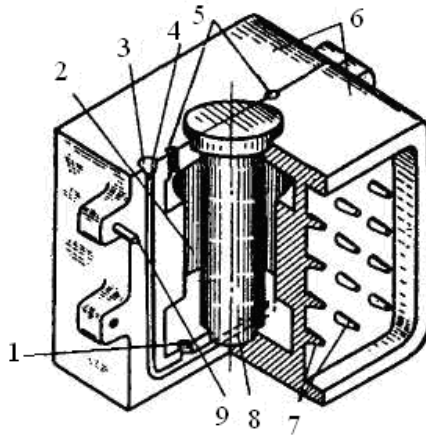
Кокіль: 1 – живильник; 2 – порожнина форми; 3 – ливникова чаша; 4 – стояк; 5 – випор; 6 – половинки кокіля; 7 – пальці; 8 – стрижень; 9 – штир
